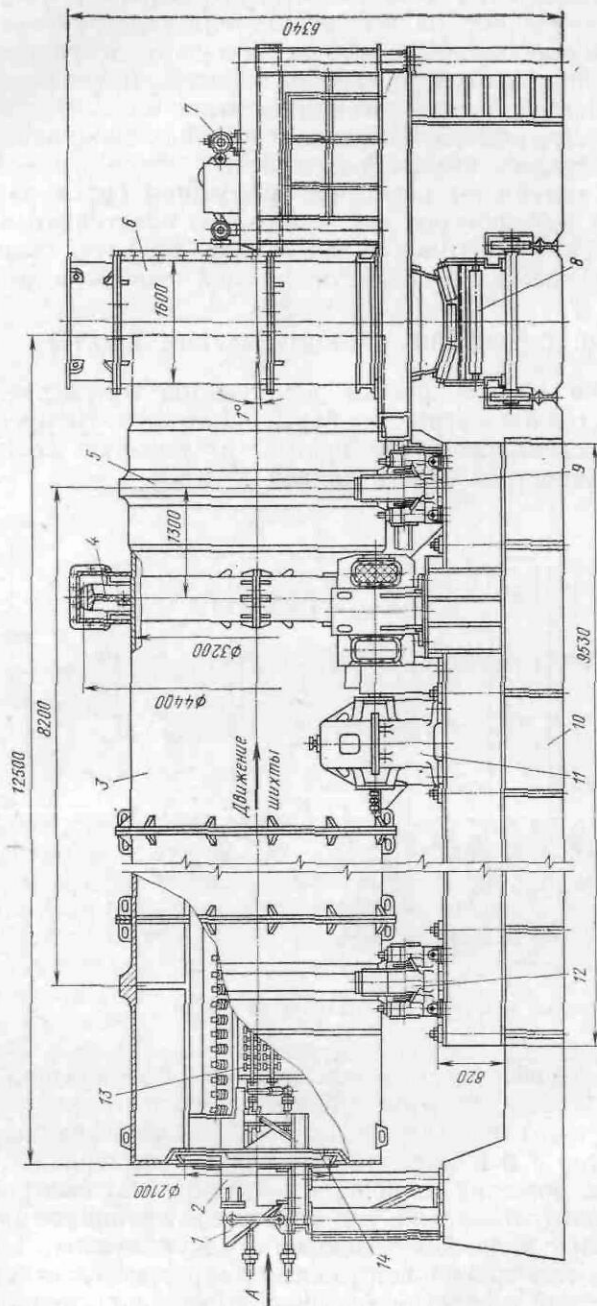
Барабанный окомкователь агломерационной шихты: 1 — качающаяся опора балки очистного устройства; 2 — балка очистного устройства; 3 — барабан; 4 — зубчатый венец; 5 — бандаж; 6 — разгрузочная камера; 7 — привод очистного устройства; 8 — оборотный конвейер; 9 — узел опорных роликов; 10 — рама; 11 — при-вод барабана; 12 — узел опорных роликов; 13 — устройство для увлажнения шихты; 14 — загрузочное отверстие
